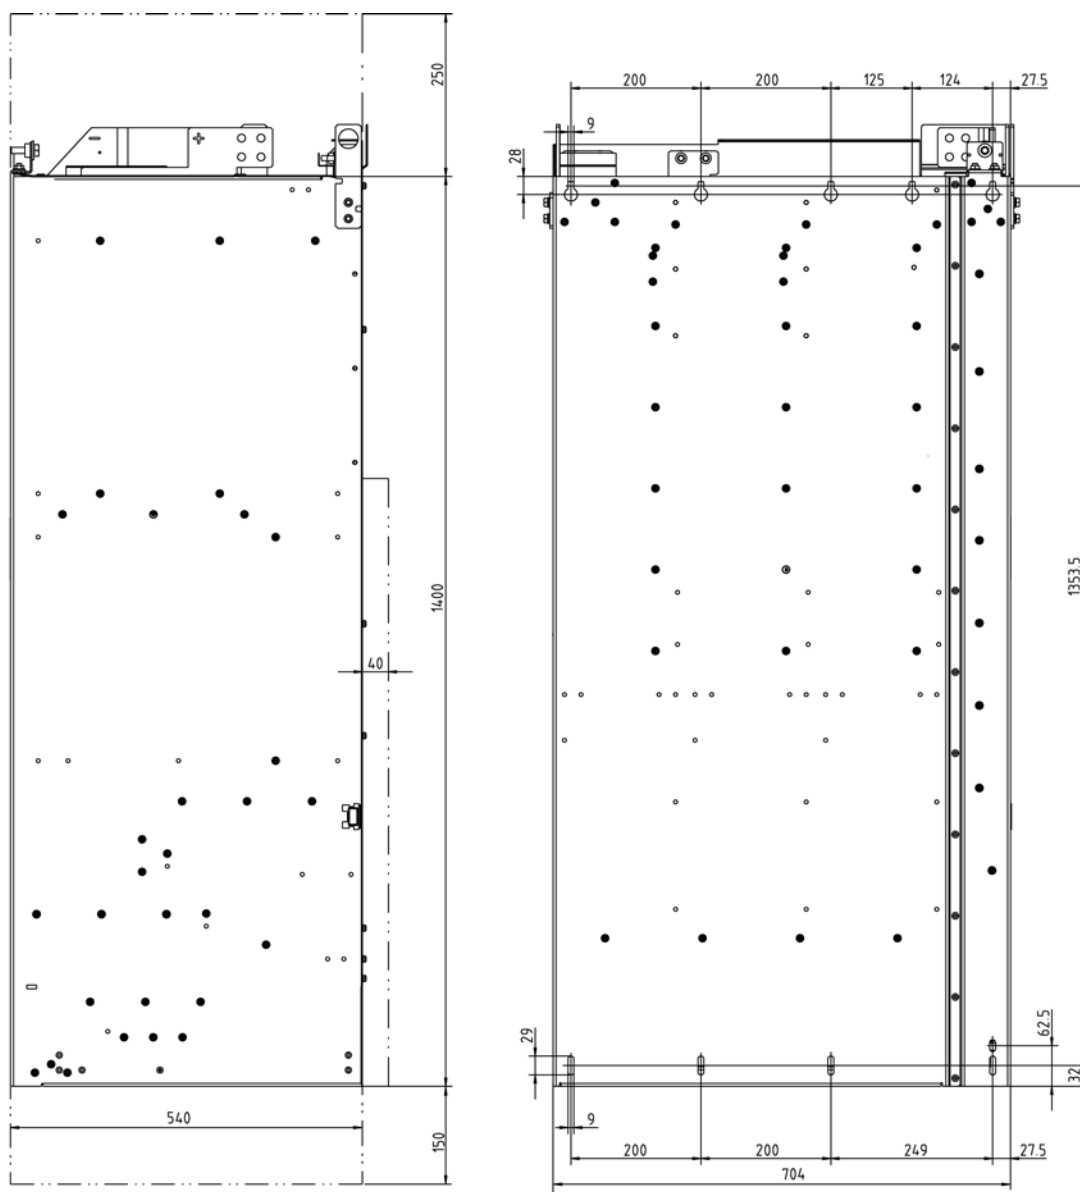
JX 型电机模块的外形尺寸图 侧视图和背视图
